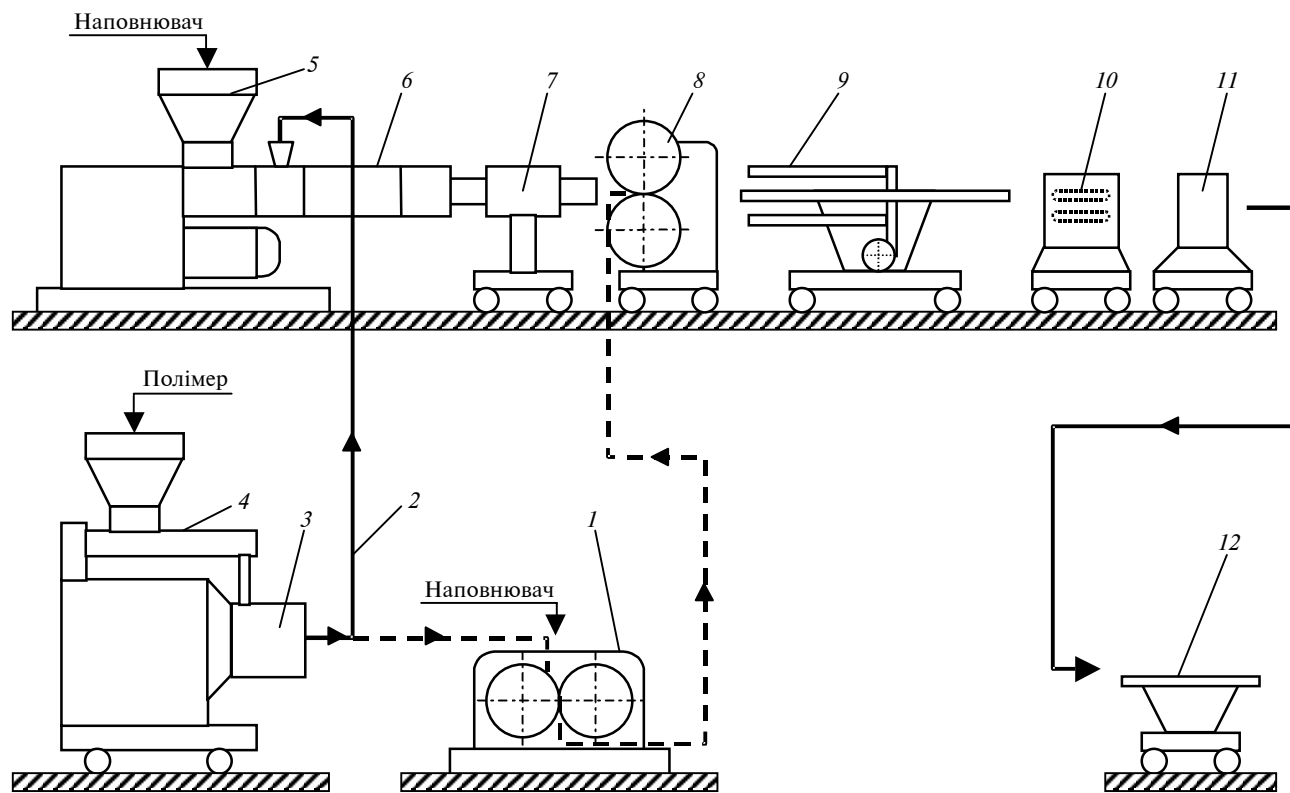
Схема модельної технологічної лінії: 1 – змішувальні вальці; 2 – розплавопровід; 3 – дисковий екструдер; 4 – живильник полімеру; 5 – дозатор наповнювача; 6 – одночерв'ячний екструдер; 7 – екструзійна головка; 8 – гладильний каландр; 9 – охолоджувальний пристрій; 10 – тяговий пристрій; 11 – пристрій поперечного різання; 12 – нагромаджувальний пристрій
